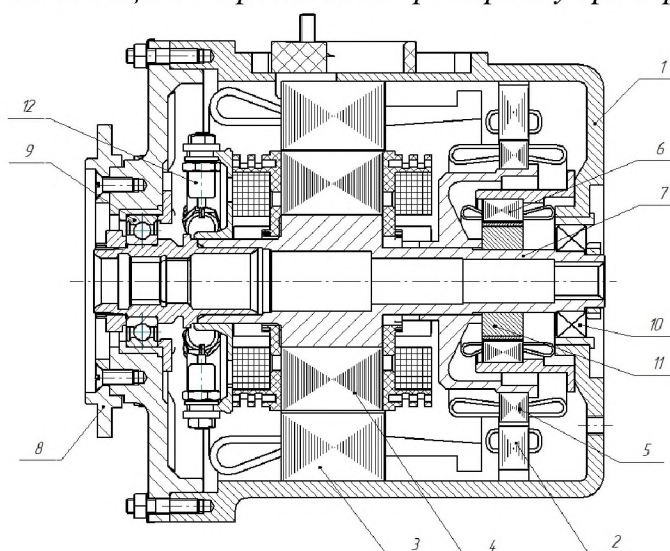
Основные узлы генератора: 1 – корпус; 2 – статор возбудителя; 3 – статор основного генератора; 4 – ротор основного генератора; 5 – ротор возбудителя; 6 – статор подвозбудителя; 7 – вал; 8 – щит; 9 – передний подшипник; 10 – задний подшипник; 11 – ротор подвозбудителя; 12 – вращающийся выпрямитель
